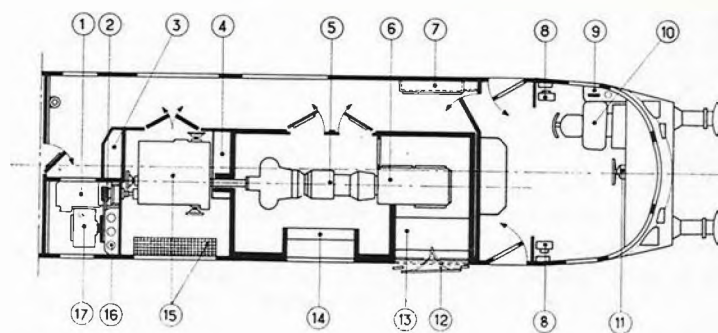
Plan d'installation de la turbine à gaz et disposition de la cabine de conduite.
